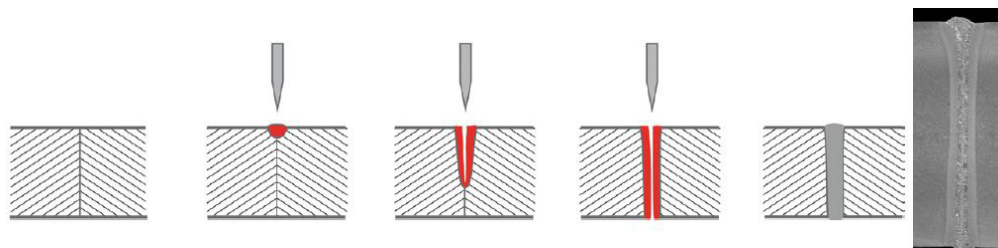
Efecto de penetración profunda: La fusión y la vaporización permiten que el haz de electrones penetre el material profundamente. El baño de soldadura (weld pool) penetra en la pieza de trabajo. Derecha: Micrografía de una soldadura de penetración completa en acero S355 de espesor 50 mm [21].
